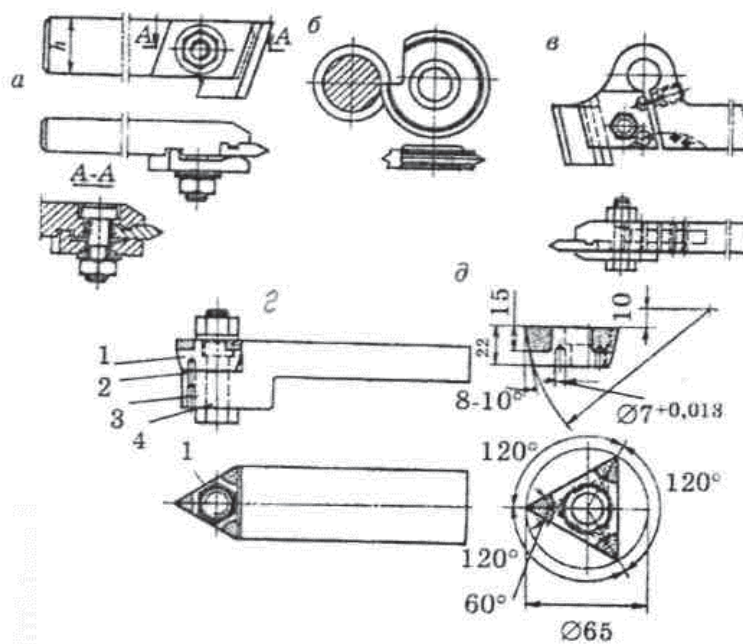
Резцы для нарезания резьбы: а – призматический; б – круглый; в – пружинная державка; г – трехгранная головка; д – трехгранная пластина; е – пластина; 1 – пластина; 2 – штифт; 3 – корпус; 4 – болт
